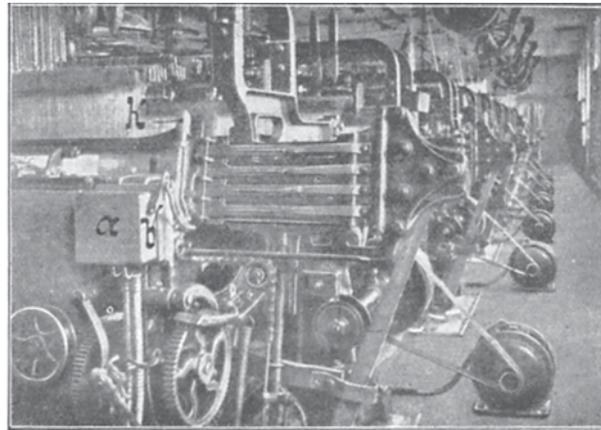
Einzelantrieb englischer Bucksinstühle.
